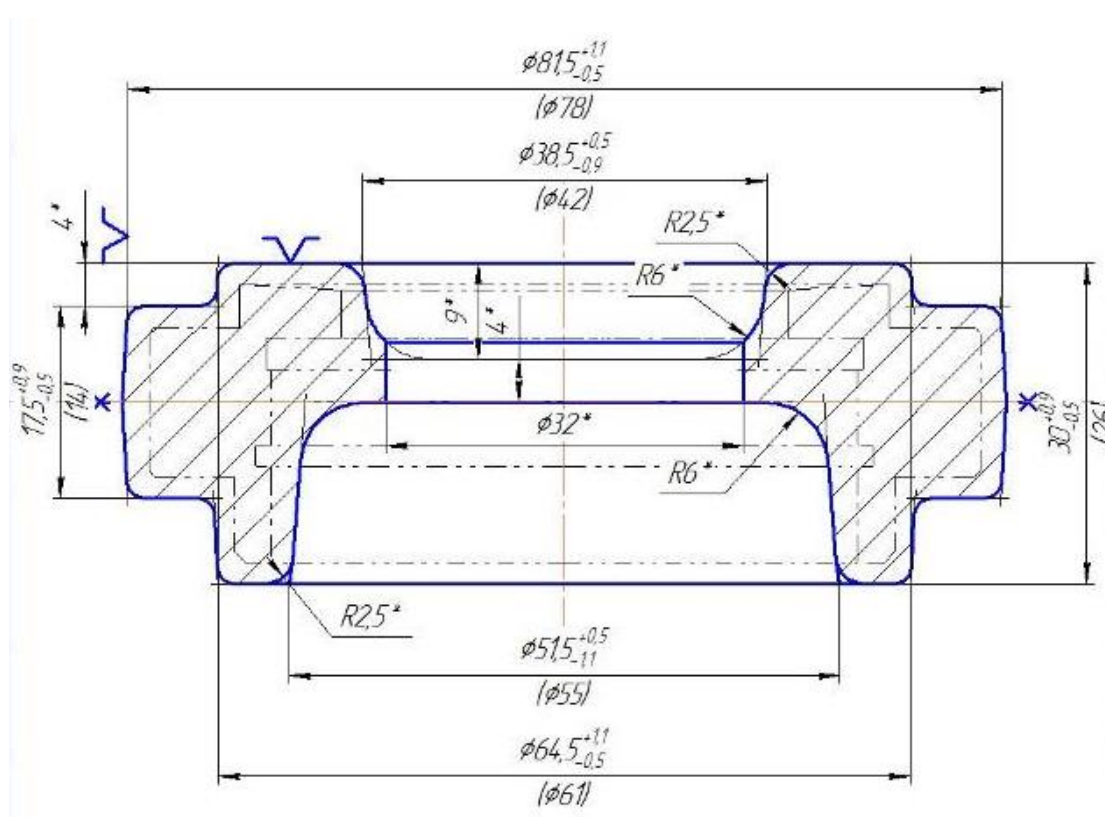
Чертеж заготовки, получаемый ковкой
